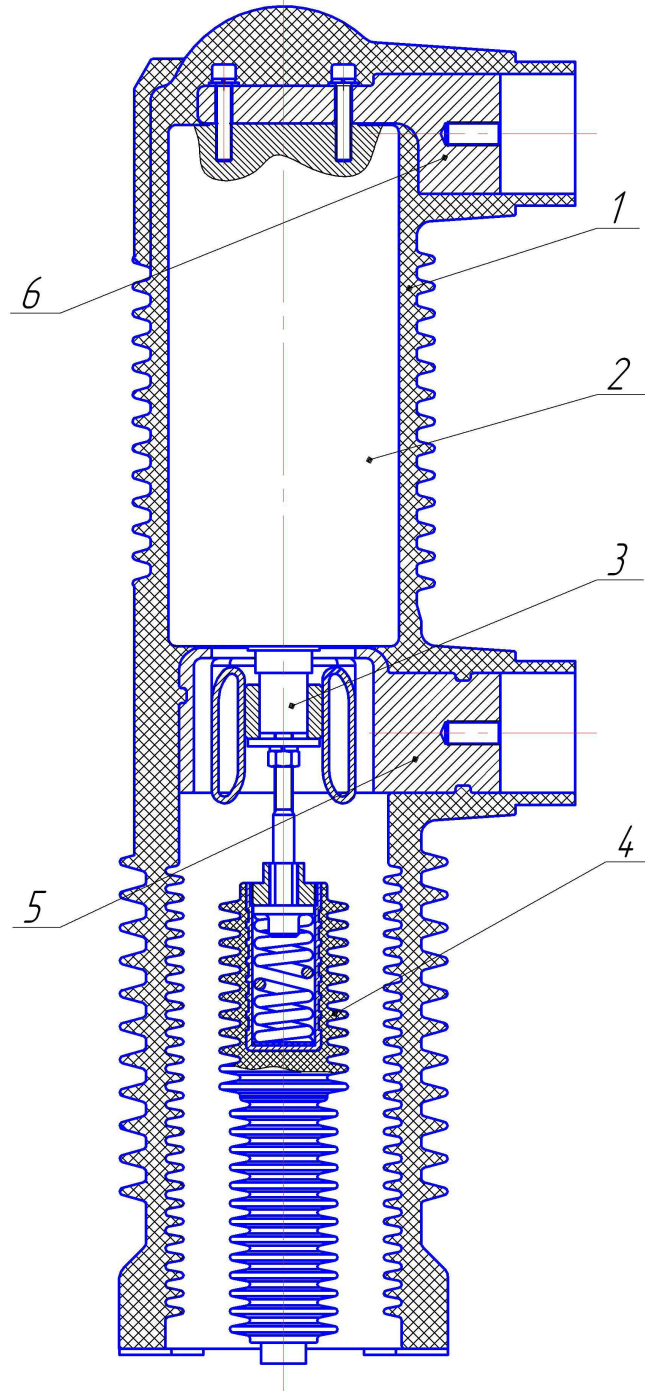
Вакуумный выключатель ВВУ-СЭЩ-П2-35
